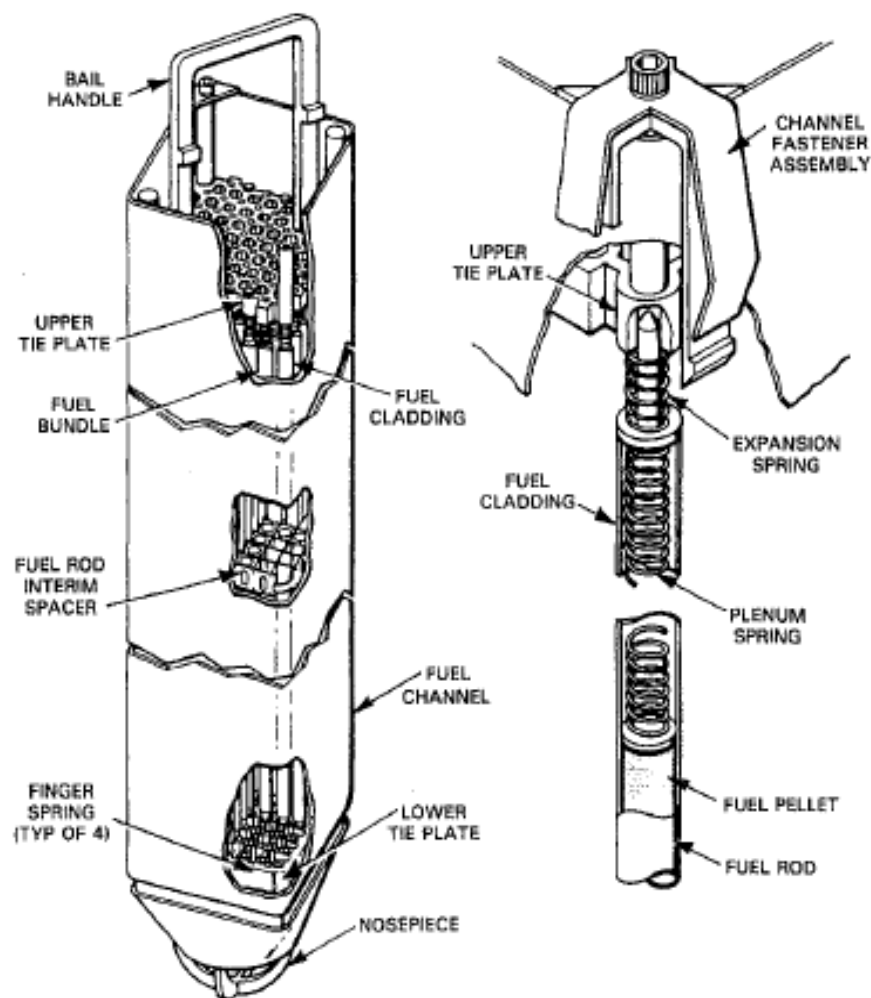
Ensamblado de combustible de un reactor BWR.
